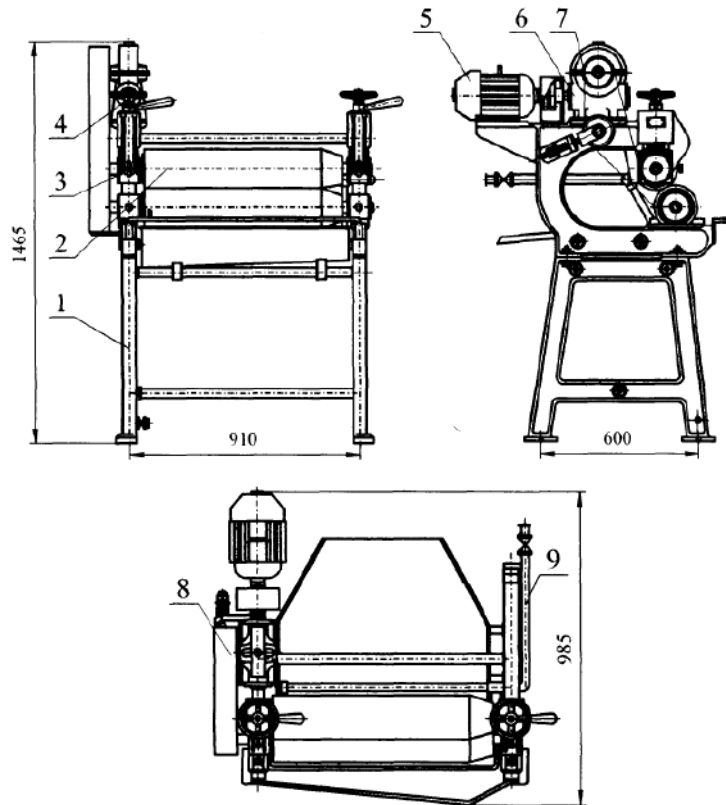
Відтискні вальці ВО-150: 1 – чавунна станина; 2 – порожнисті циліндри; 3 – рухомі підшипникові опори; 4 – маховик гвинтового механізму; 5 – електродвигун; 6 – черв'ячний редуктор; 7 – ланцюгова передача; 8 – кожух; 9 – трубопровід подачі води
